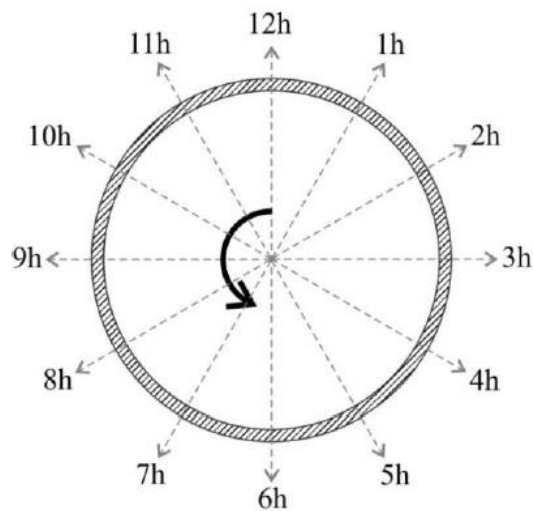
Posições de soldagem convencionadas ao longo do tubo. [Adaptado de 12]
